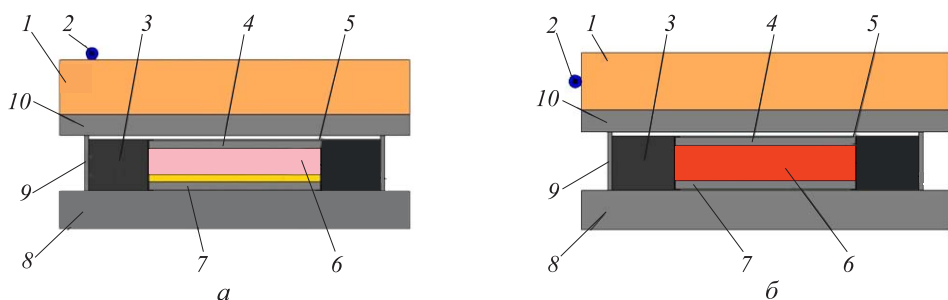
Схемы взрывного компактирования цилиндрических заготовок:
